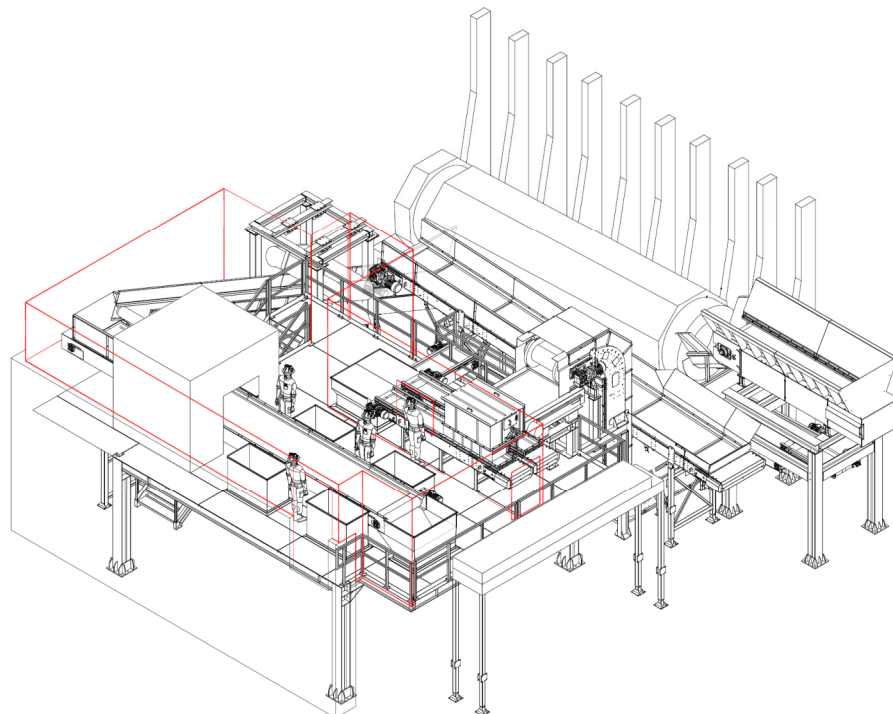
ricostruzione 3D dell’impianto selezione rinfuse metalliche
